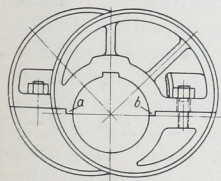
Doppel-exzenter mit kegeligen Laufflächen.
